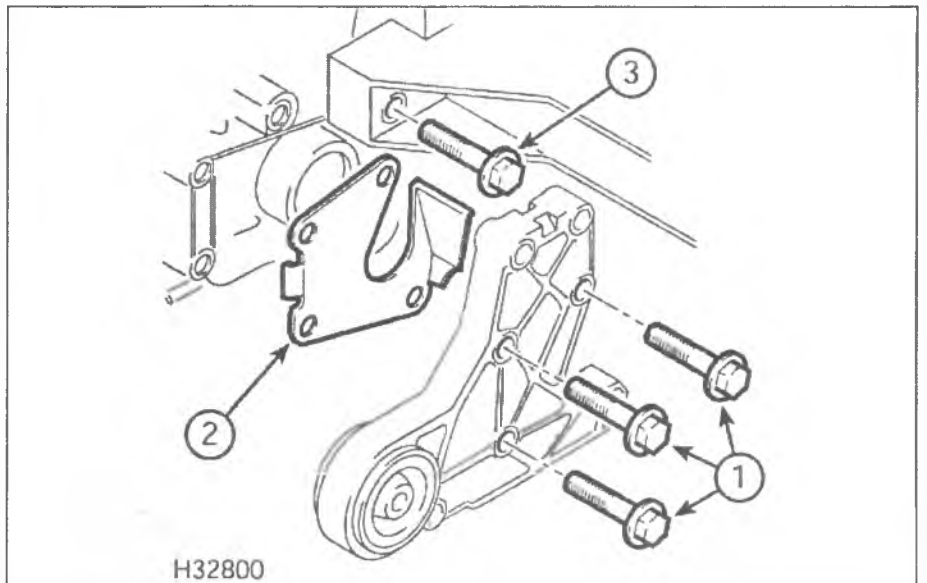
Болты соединительной пластины раздаточной коробки (1), крышка маховика (2) и призонный болт (3)
